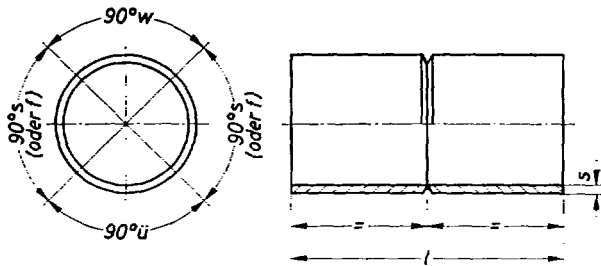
Stumpfnah-Prüfstück für Rohrschweißer in Schweißposition w, s, ü (Maße siehe Tabelle 7)
